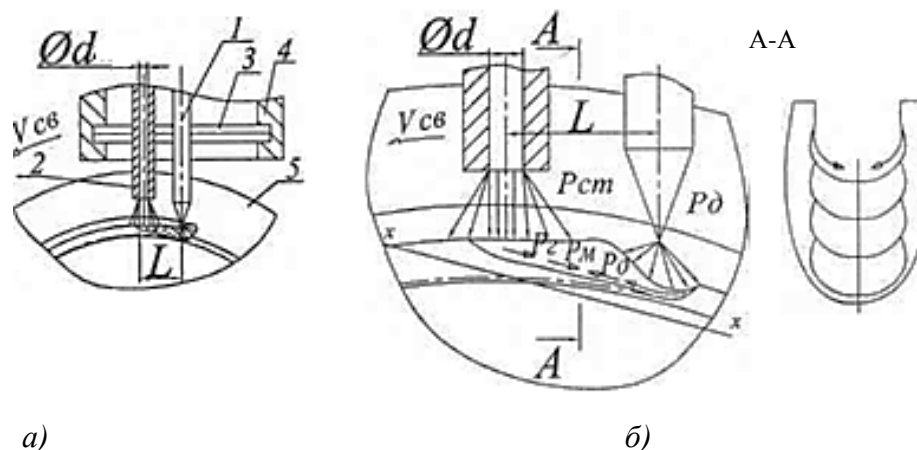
Схема процесса сварки специальной горелкой (а) и расположения сил в сварочной ванне (б):
